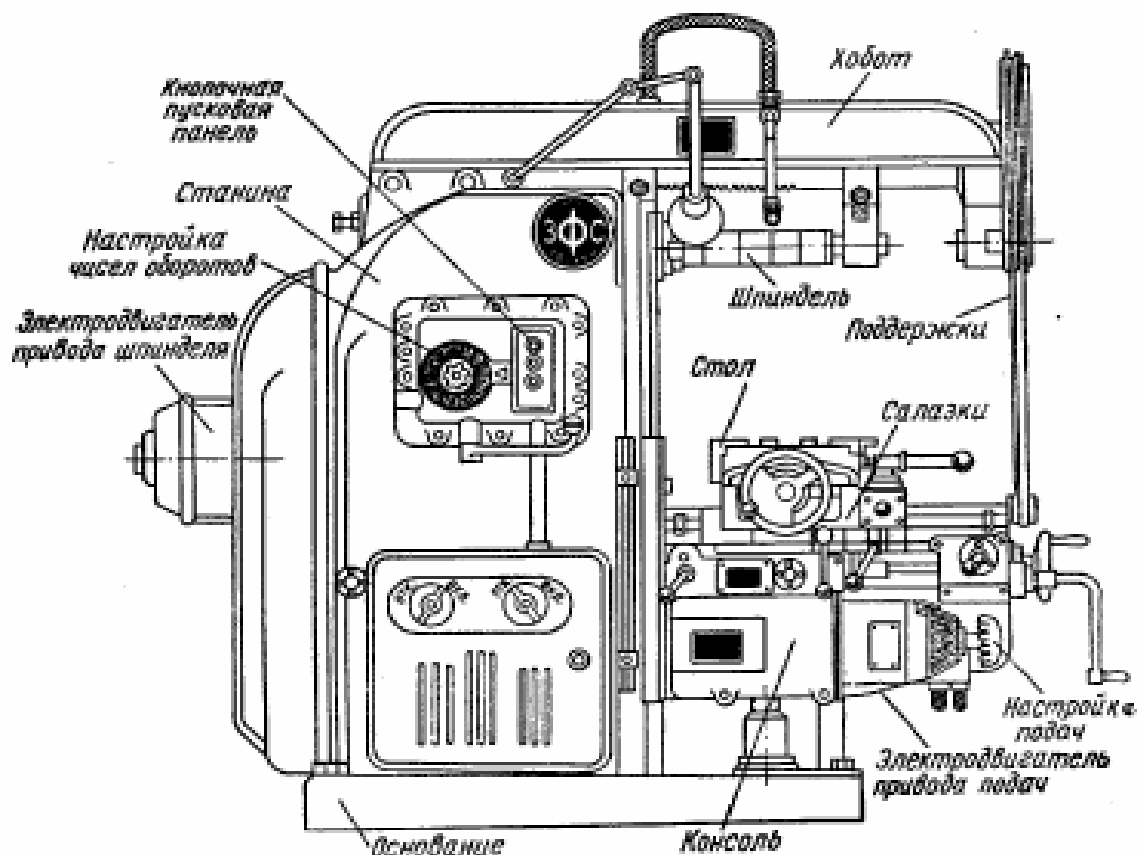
Горизонтально-фрезерный станок 6H82Г
